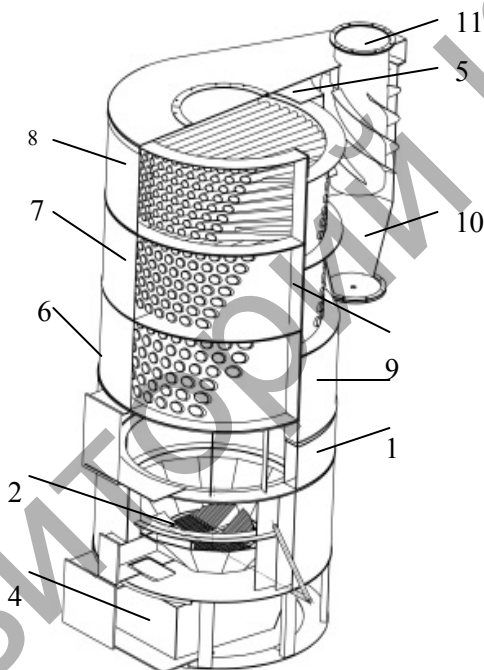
Общий вид теплообменного модуля Е.Н.Воронова: 1 — корпус; 2 — конусообразное топочное устройство; 3 — загрузочное кольцо; 4 — под топочного устройства; 5 — коллектор дымовых газов; 6 — нижний модуль нагревательных элементов с диаметром трубок  $d_{\text{тр}} = 60 \times 4,5$  мм; 7 — средний модуль нагревательных элементов с диаметром трубок  $d_{\text{тр}} = 52 \times 3,5$  мм; 8 — верхний модуль нагревательных элементов с диаметром трубок  $d_{\text{тр}} = 42 \times 3,5$  мм; 9 — сборно-распределительные водяные коллекторы («водяная рубашка»); 10 — циклон газоочистки; 11 — выход дымовых газов
